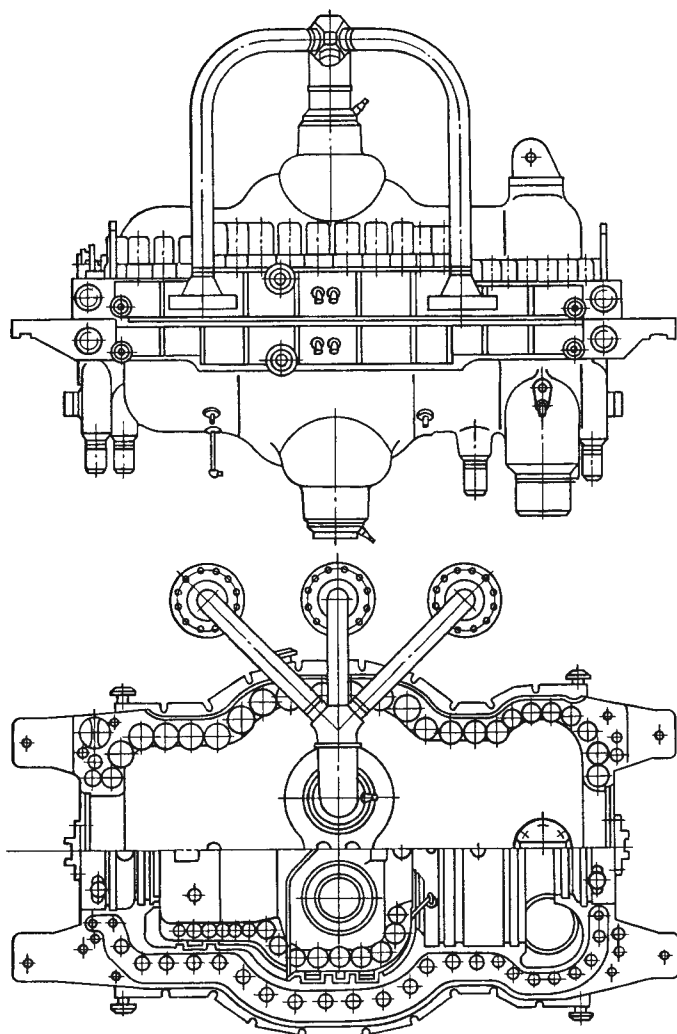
Корпус ЦВД турбины К-300-23,5 ЛМЗ
